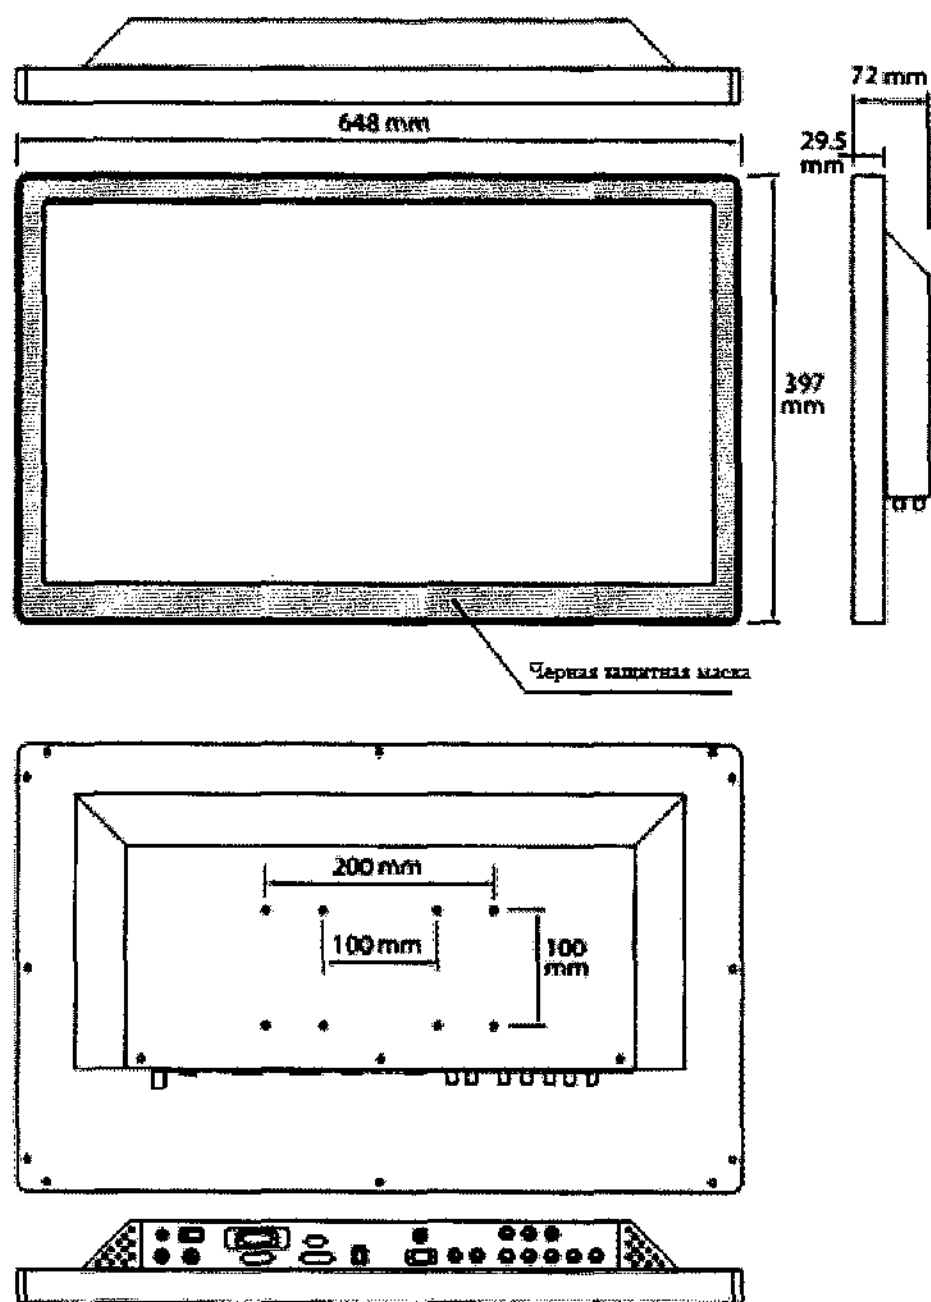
Габаритный чертеж Мониторов FS-L2701D и FS-L2701DT
